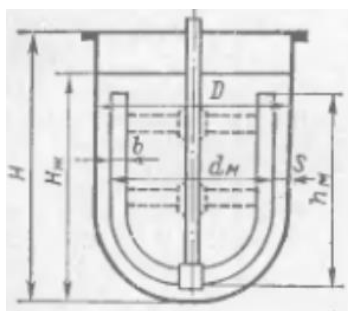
Схема ємнісного реактора з якірною мішалкою
